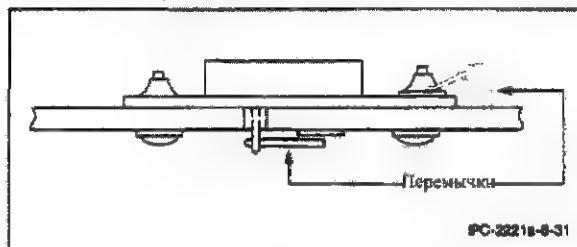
Металлический мощный корпус с неподатливыми выводами
